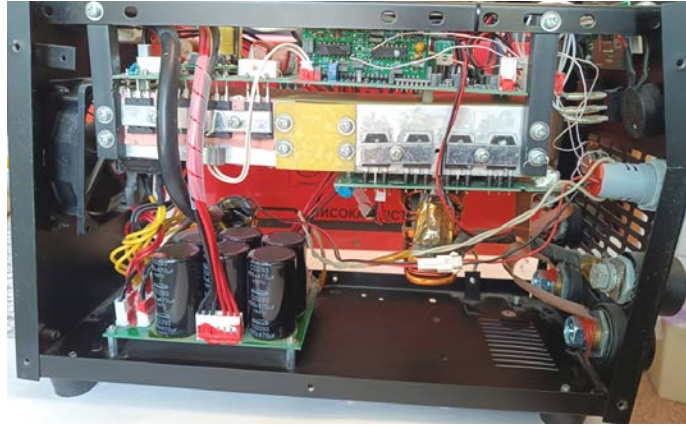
Внутрішня компоновка елементів і блоків зварювального інвертора
